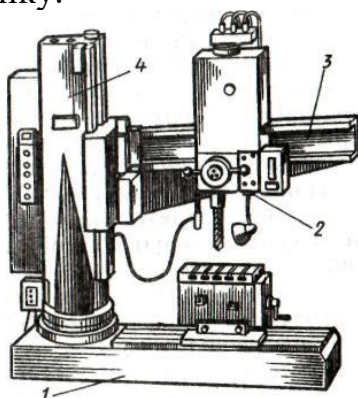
Общий вид радиально – сверлильного станка модели 2554
